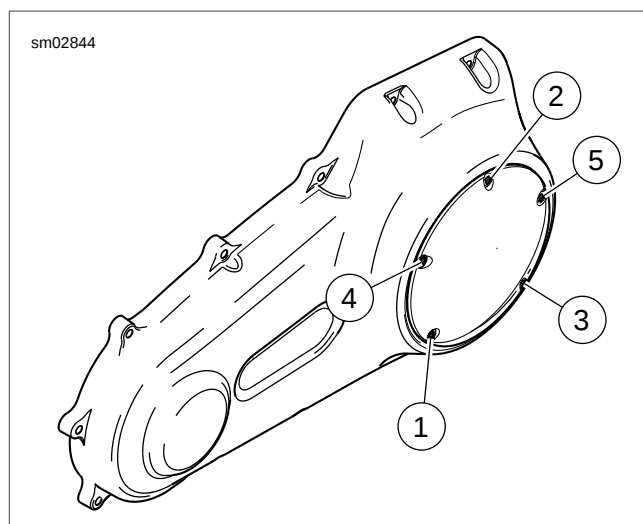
Séquence de serrage de couvercle d'embrayage
